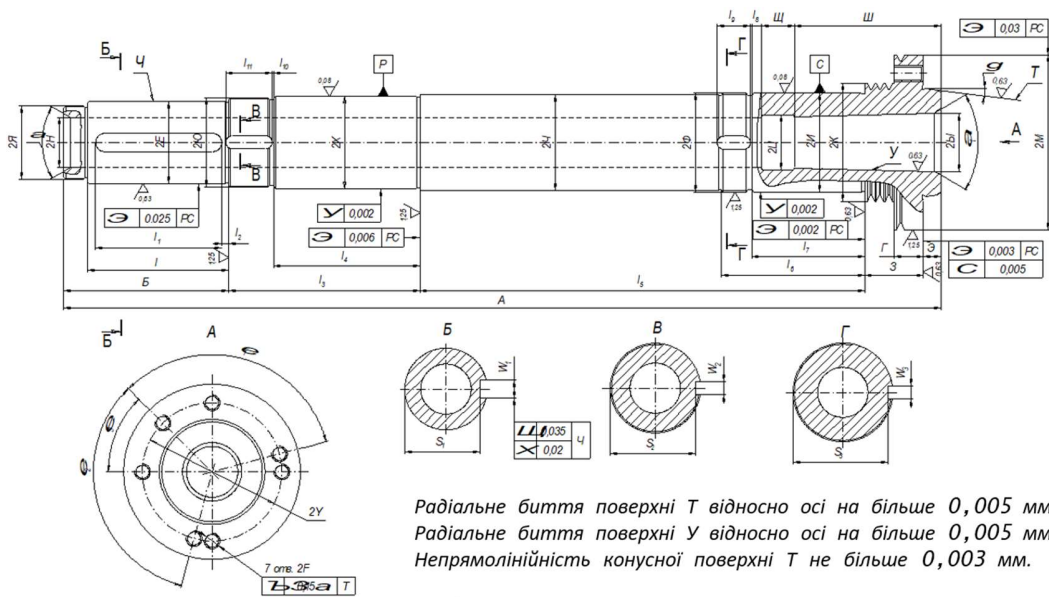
Вибір баз для оброблення поверхонь
